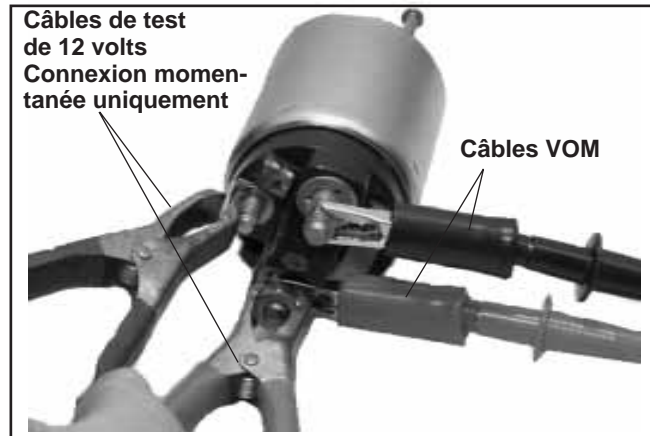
Test de continuité de contact de la bobine d'engagement /solénoïde.
